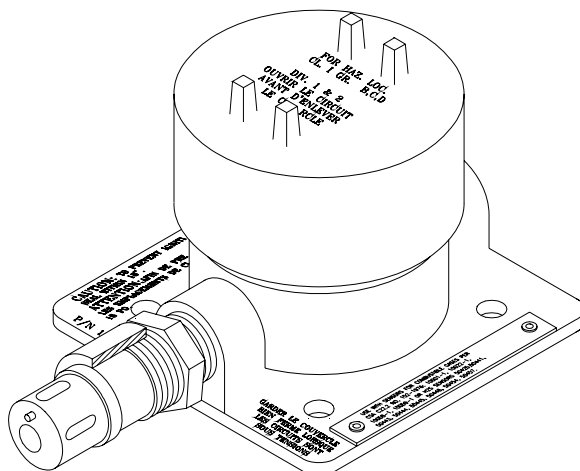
Универсальный защитный корпус датчика с установленным датчиком и брызгозащитным колпачком
